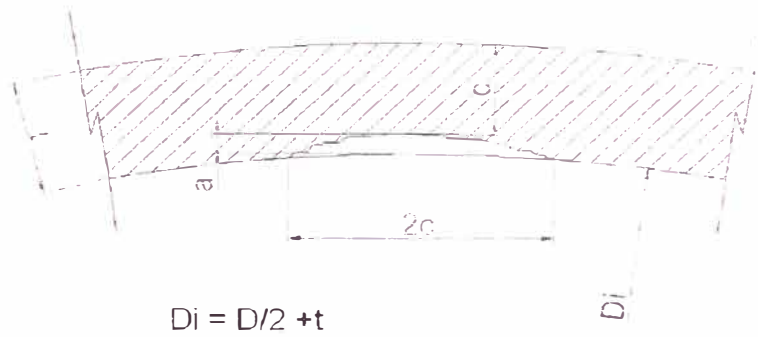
Esquematzación de la caracterización de las dimensiones relevantes de una discontinuidad plana en una unión soldada.
